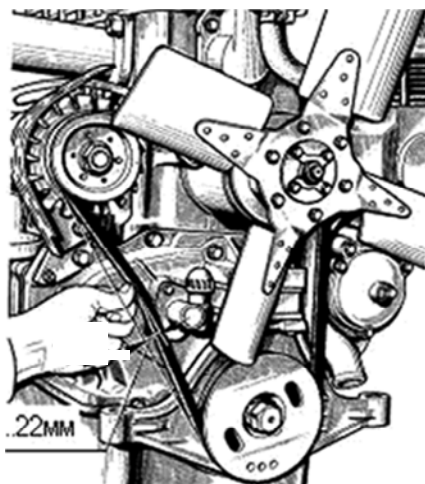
Проверка натяжения ремня вентилятора [30]
